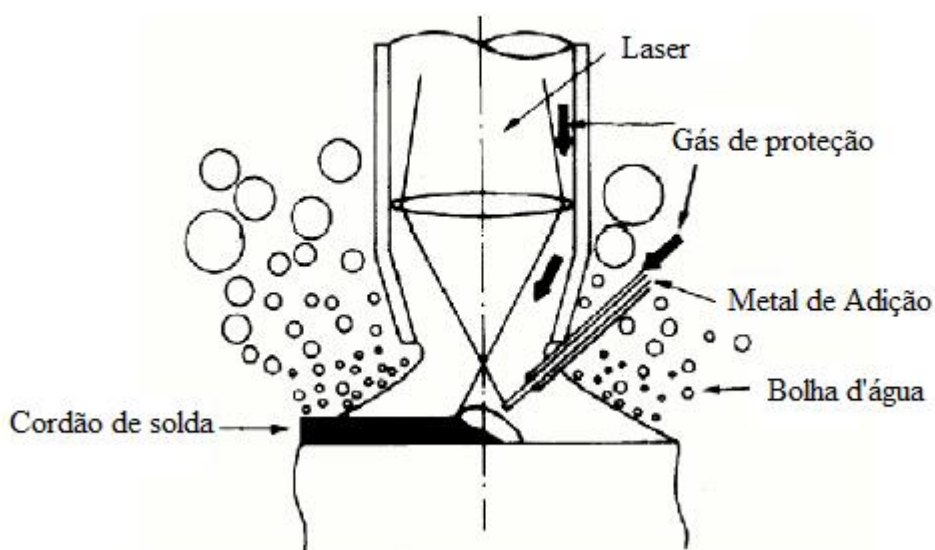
3 – Representação esquemática do processo de soldagem a laser [3].
